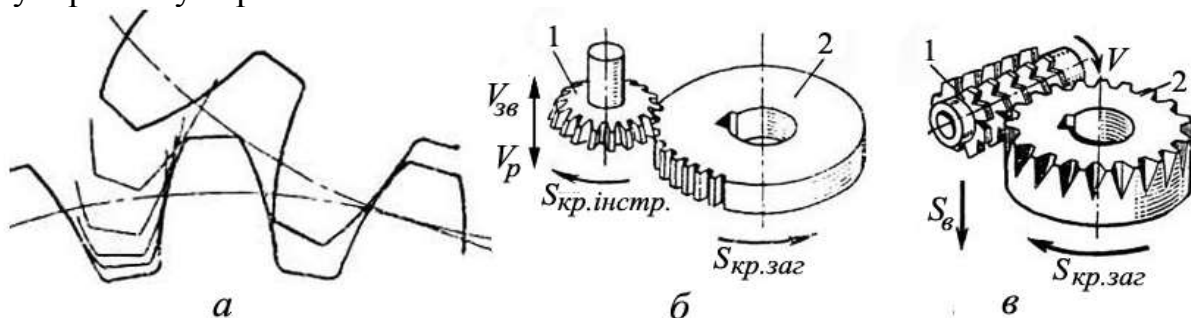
Нарізання зубців циліндричного зубчастого колеса методом обкату
